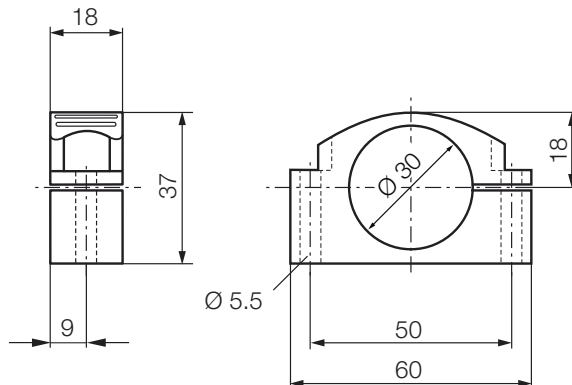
Collier de fixation BTL6-A-MF03-K-50
